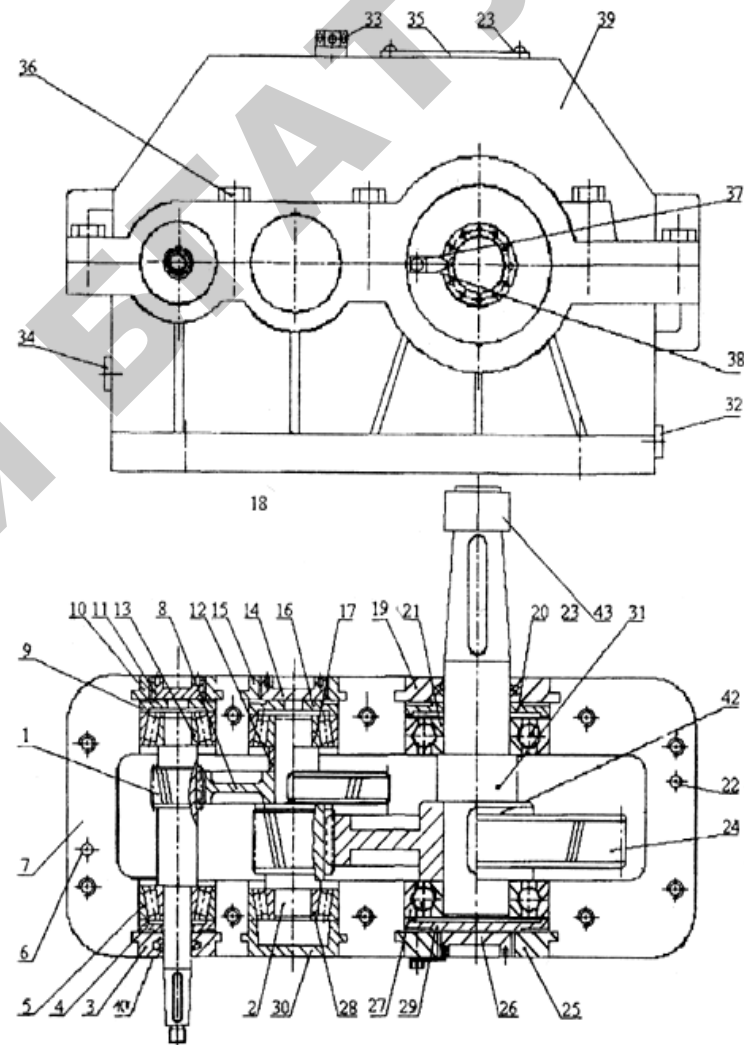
Двухступенчатый зубчатый цилиндрический редуктор
